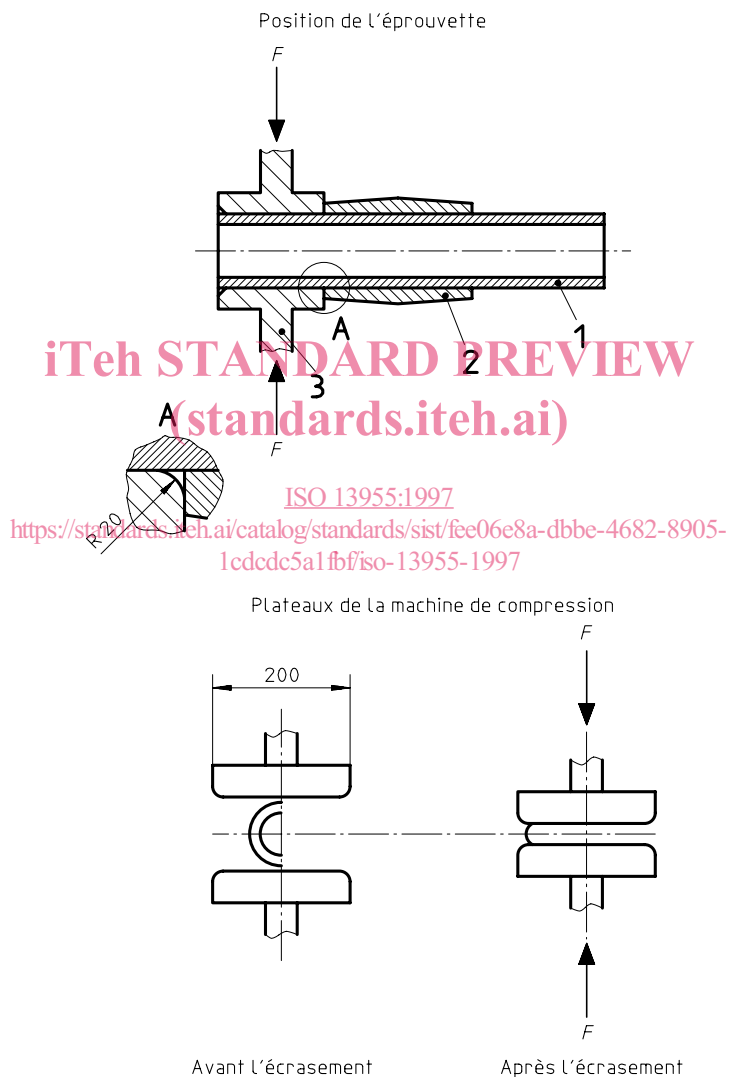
Examen de la décohésion d'une éprouvette comportant une emboîture électrosoudable
